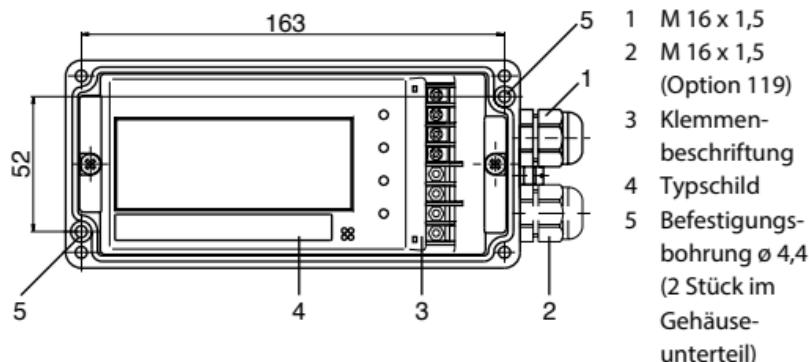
Frontansicht ohne Gehäusedeckel
